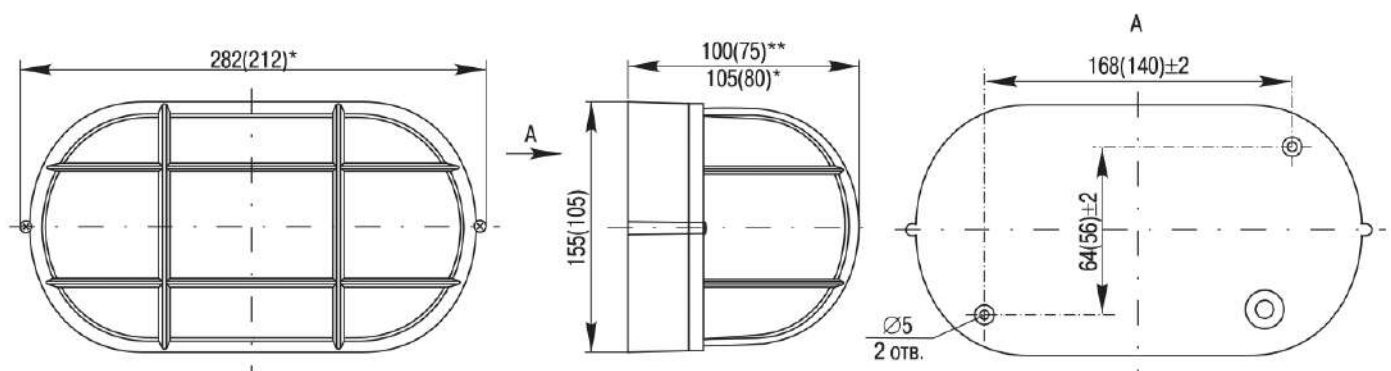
Габаритные и установочные размеры светильников НПП 1202...1208
